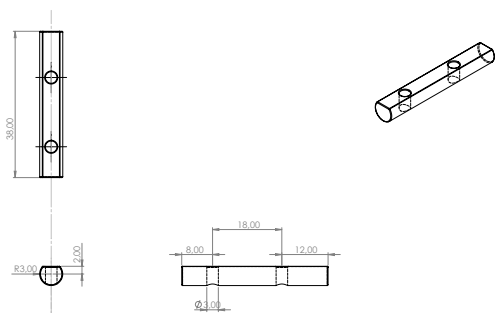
Desenho técnico - *String tree* para Braço Aço.
